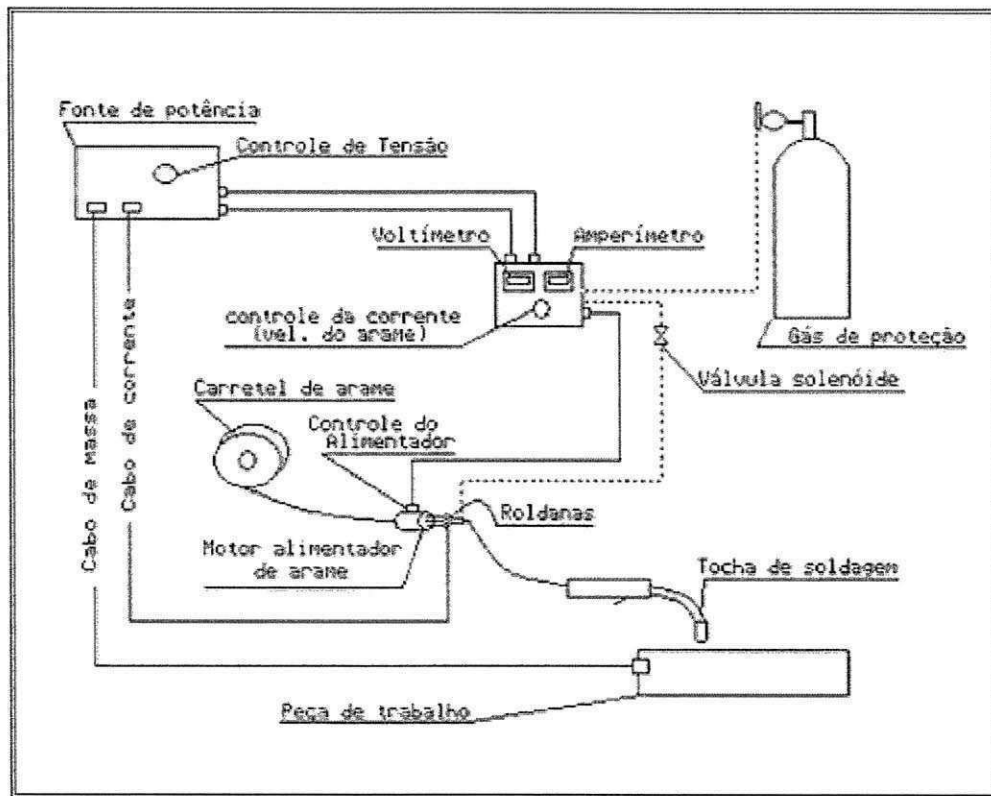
Equipamento básico para soldagem com arame tubular.
